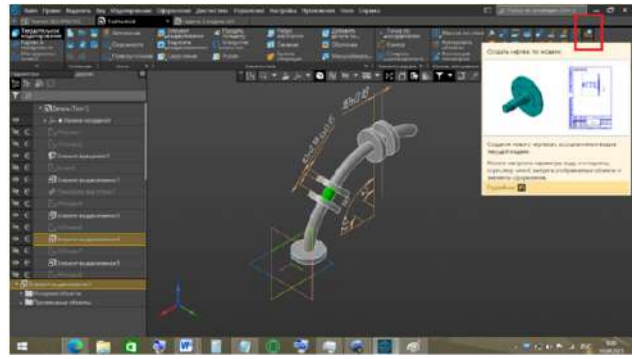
Расположение кнопки «создать чертёж по модели»
